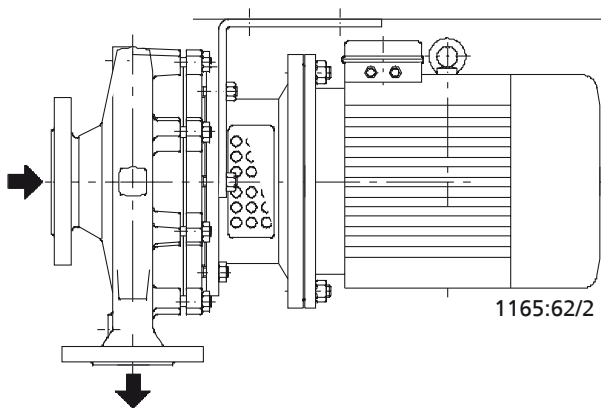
Pumpenfuß Befestigung oben, bis Motorgröße 112 = 4 kW
